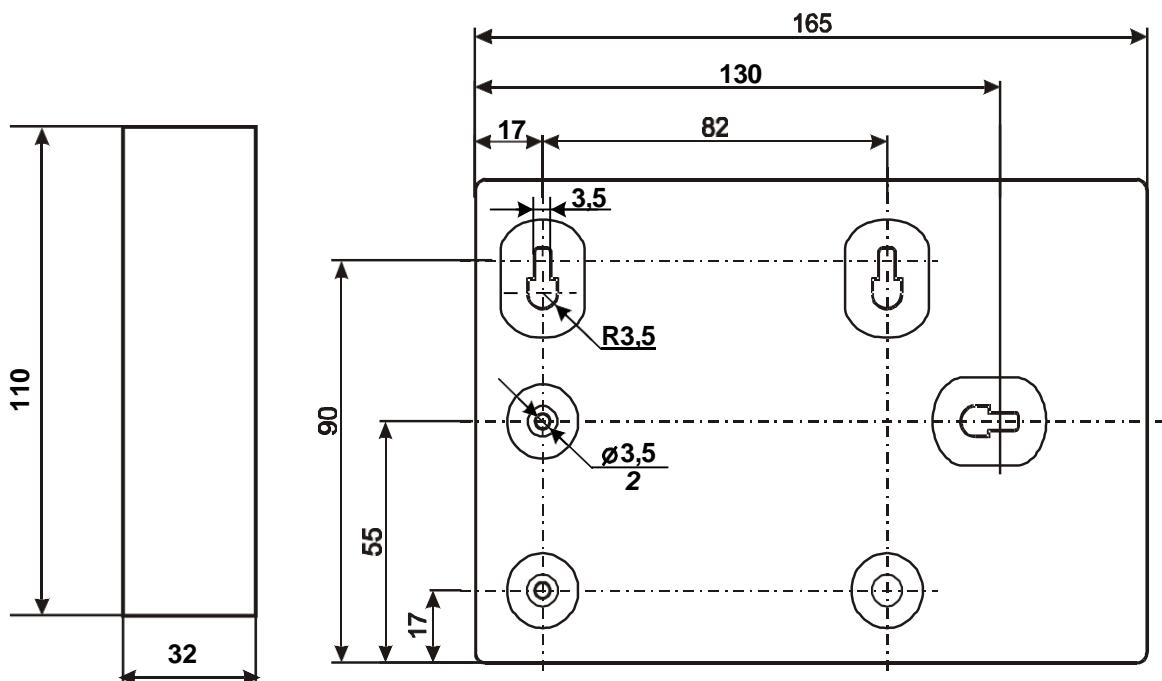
Габаритные и присоединительные размеры корпуса ТИ
